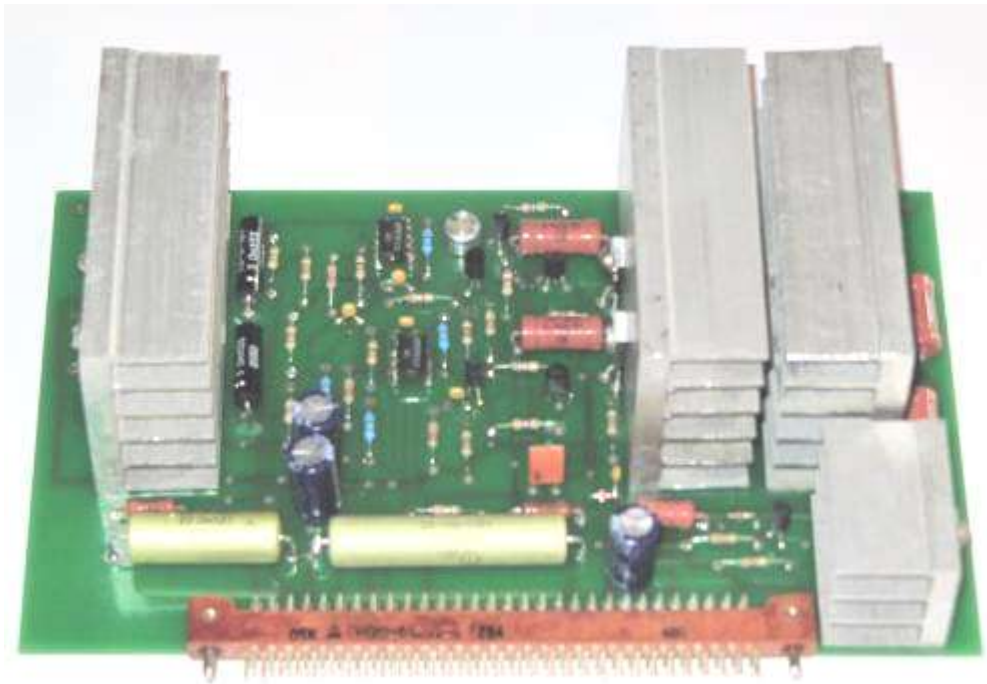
Загальний вигляд плати перетворювачів напруга-струм
